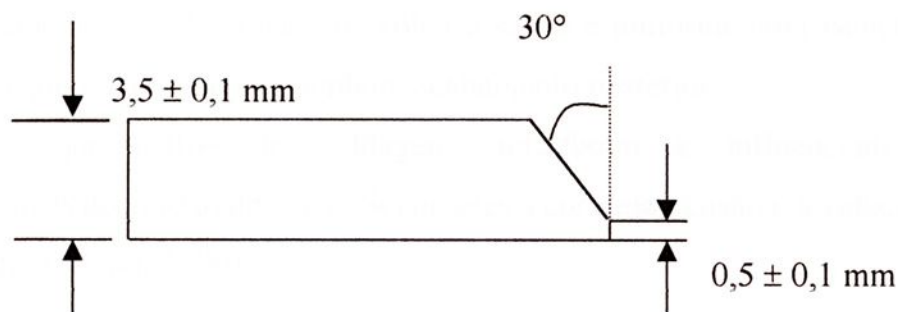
Detalhe do chanfro realizado para soldagem das chapas.
